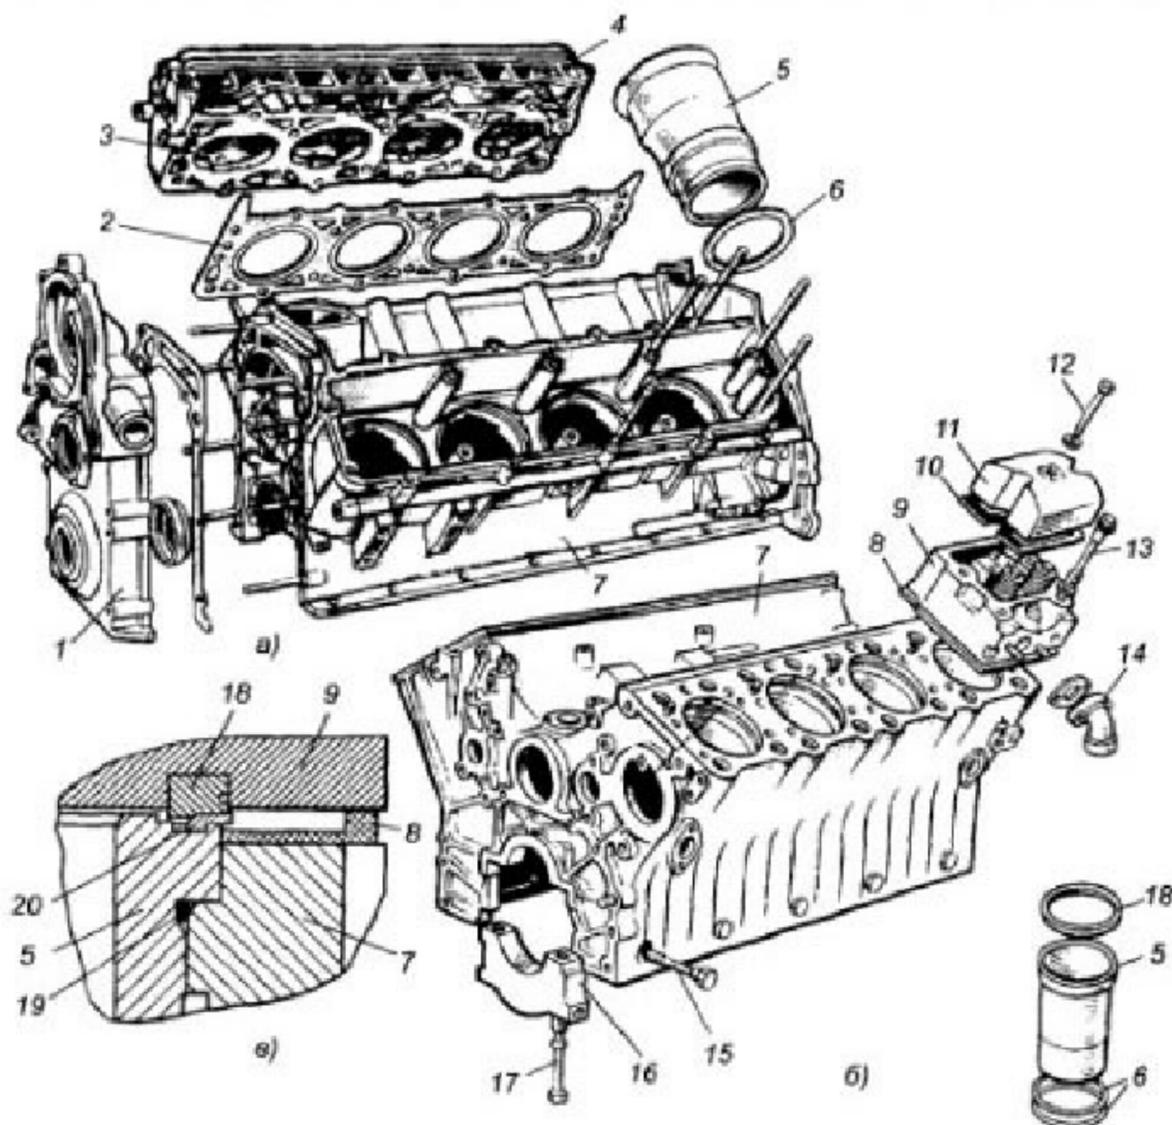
Блок-картер: а — V-образного карбюраторного двигателя; б — V-образного дизельного двигателя; в — соединение головки блока цилиндров, гильзы и блока цилиндров двигателя КаМАЗ-740; 1- крышка блока распределительных зубчатых колес; 2 — прокладка головки блока цилиндров; 3 — камера сгорания, 4 — головка блока цилиндров, 5 — гильза цилиндра; 6 и 19 — уплотнительные кольца, 7 — блок цилиндров; 8 — резиновая прокладка; 9 - головка блока цилиндров; 10 - прокладка крышки; 11 - крышка головки блока цилиндров; 12 и 13 — болты крепления крышки и головки блока цилиндров; 14 — патрубок выпускного коллектора; 15 — болт-стяжка; 16 — крышка коренного подшипника; 17 — болт крепления крышки коренного подшипника; 17 - стопорное кольцо; 20 — стальная прокладка головки блока цилиндров.
